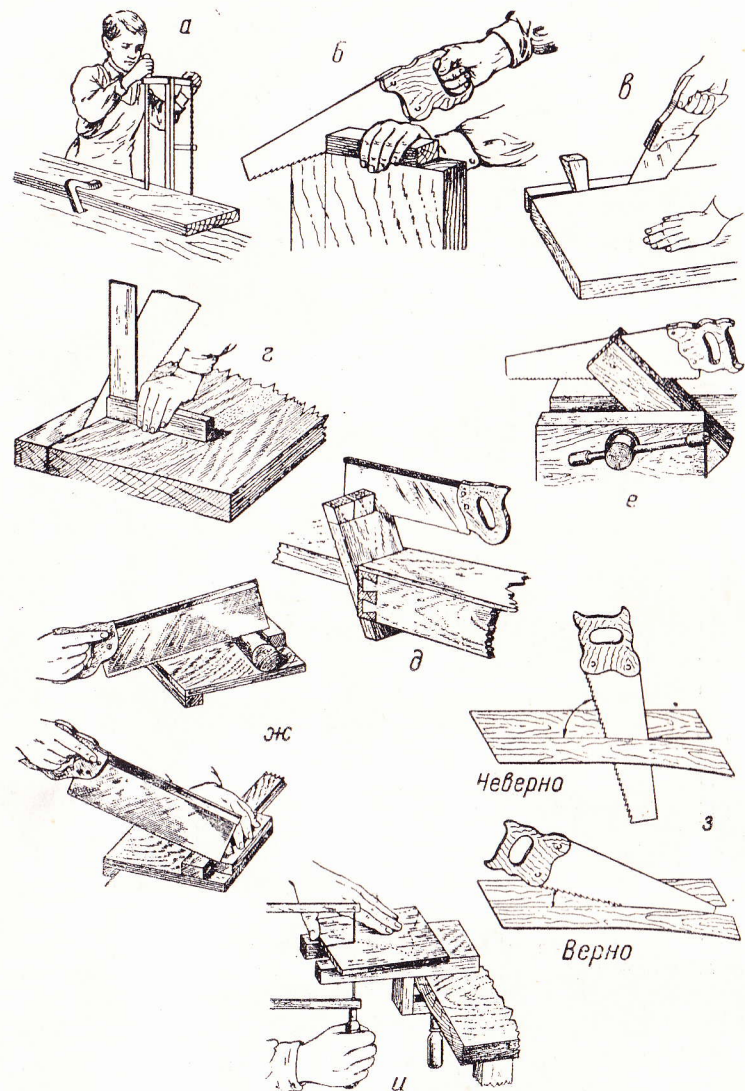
Приемы работы пилами: а — распашное пиление; б — как начинать пропил; в — расклинивание пропила; г — проверка положения полотна ножовки по угольнику; д — зашлифовывание шипов; е — пропиливание вдоль пластин; ж — пиление с упором; з — пиление фанеры; и — выпиливание лобзиком.
